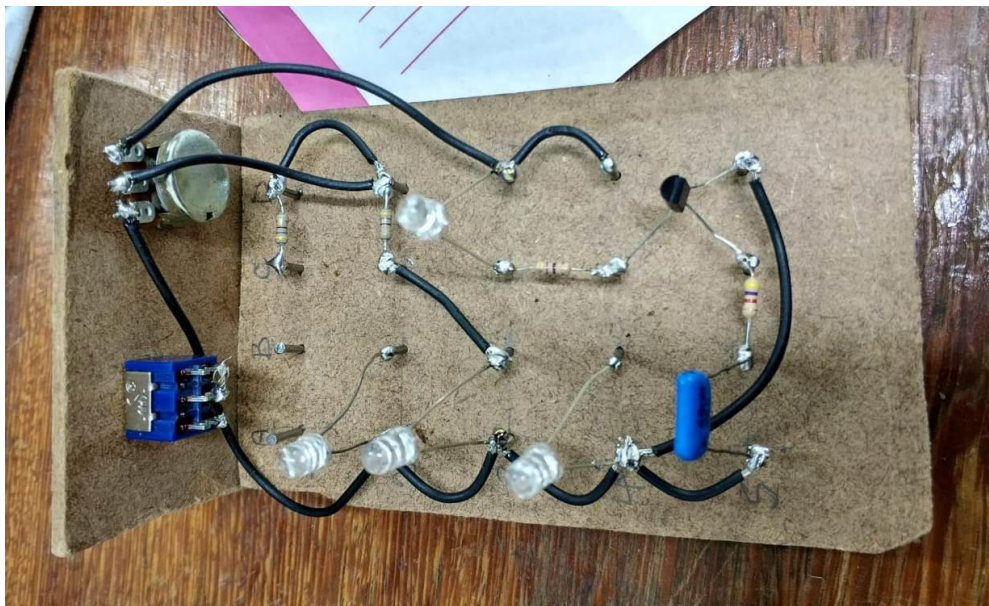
Soldagem dos Condutores Necessários (Parte II)
